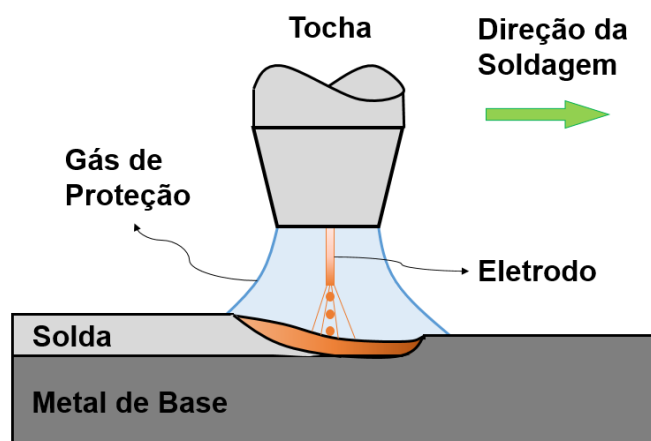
Processo de soldadura MIG/MAG.
